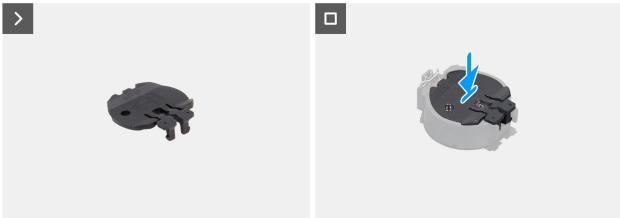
Instalación de la cubierta de la batería de tipo botón
